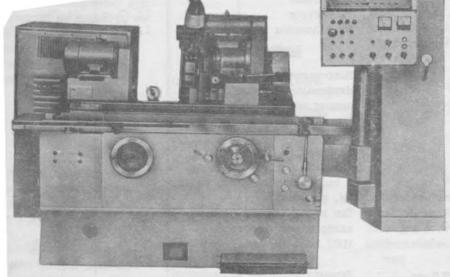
Рис. I. Станок универсальный круглошлифовальный ЗУІЗУВФІО
